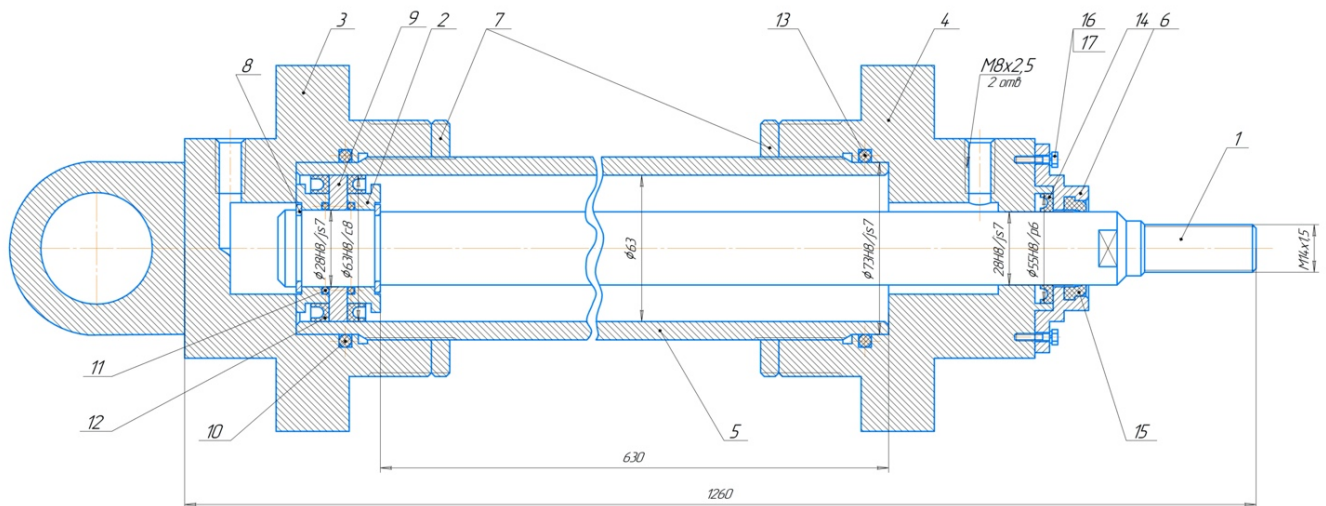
Чертеж поршневого гидроцилиндра
